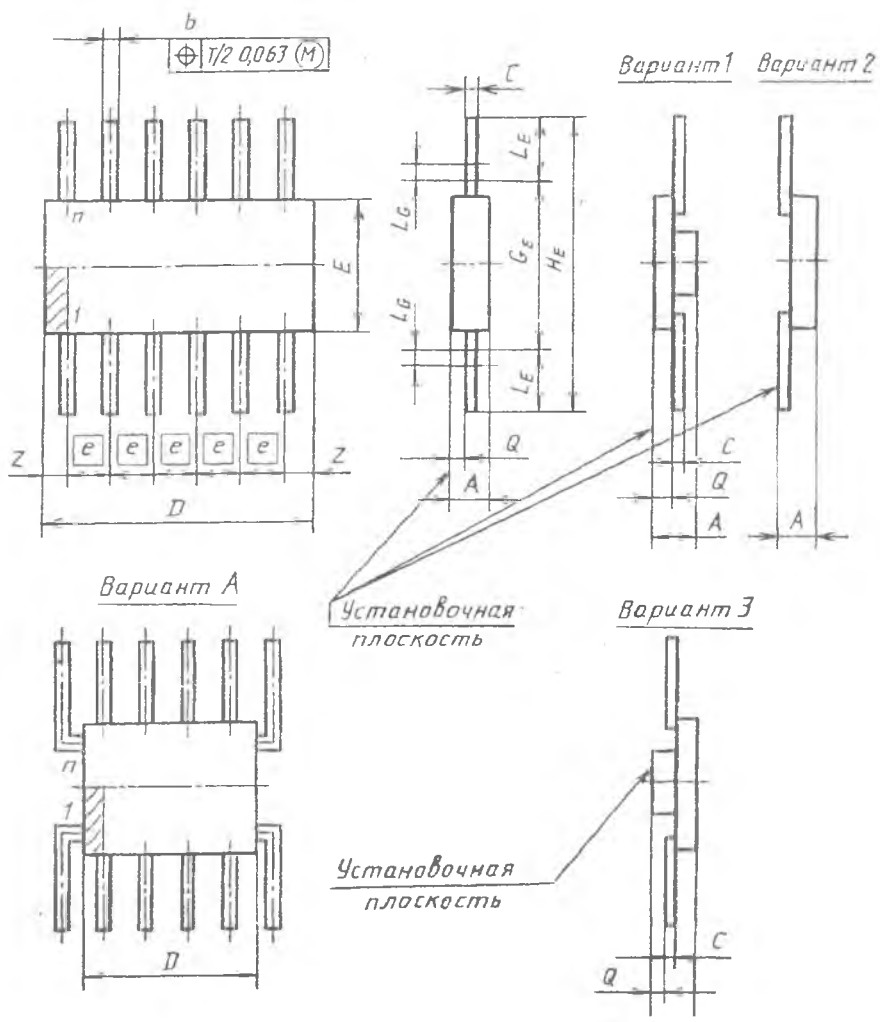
Конструкция корпуса типа 4 подтипа 1
